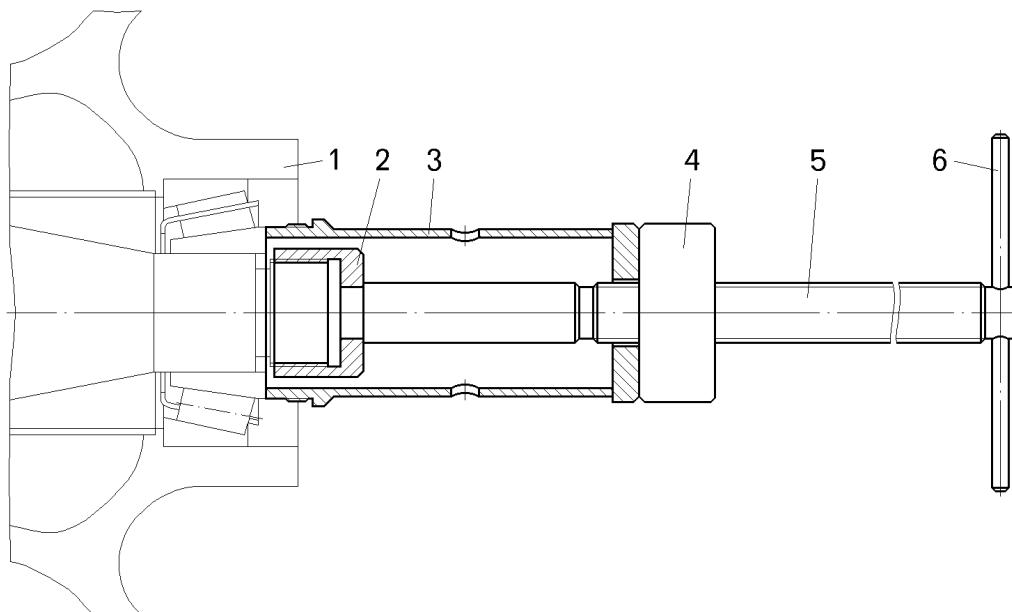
Приспособление для запрессовки ступицы переднего колеса:
